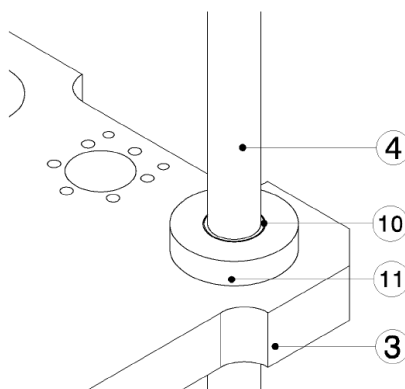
Vista isométrica superior da plataforma e outros componentes; 3- plataforma; 11- casquilho adaptador; 10- casquilho deslizante; 4- varão.
